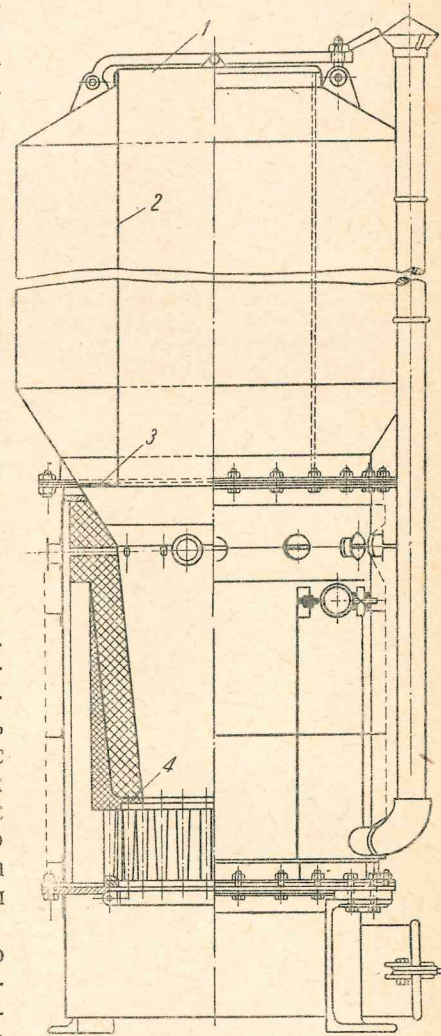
Газогенератор ЦНИИВТ-3, приспособленный для работы на швырке
